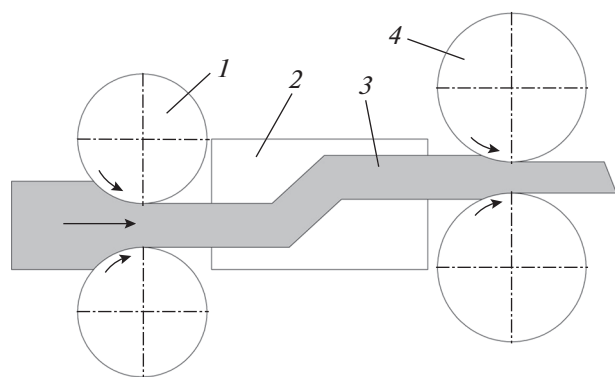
Схема совмещенного процесса “прокатка–РКУ-прессование”: 1 – первая пара валков с гладкой бочкой; 2 – матрица; 3 – заготовка; 4 – вторая пара валков с гладкой бочкой.
